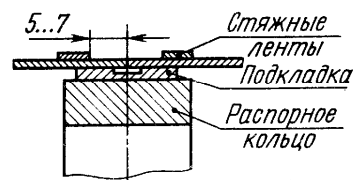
Сборка обечаек под сварку кольцевых швов
